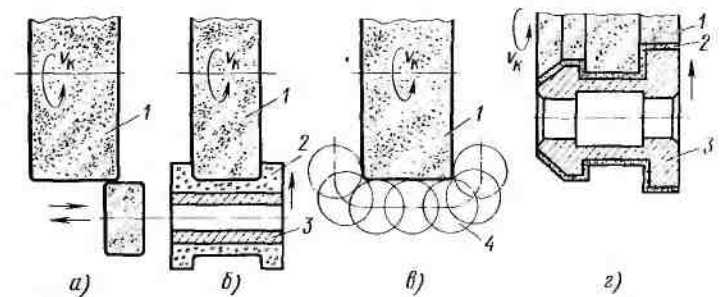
Схемы правки шлифовальных кругов алмазными роликами:
